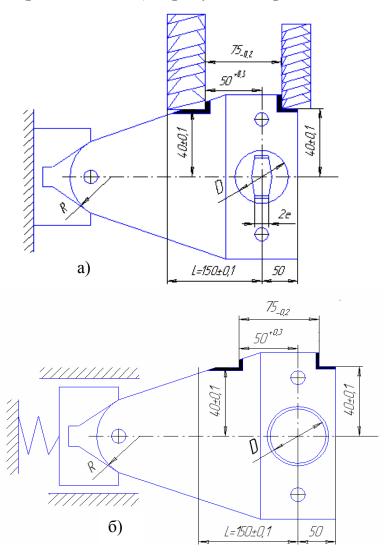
Схема базирования заготовки: а — на жесткую призму и срезанный ромбический штифт; б — на податливую призму и цилиндрический штифт
